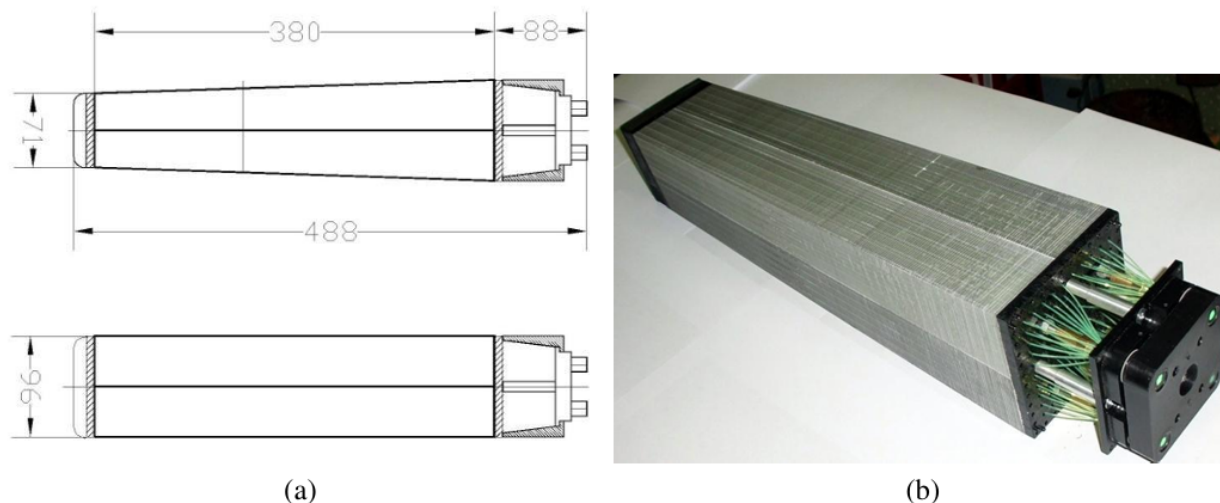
Чертеж отдельного модуля калориметра (a) и фото модуля без внешнего корпуса (b)
